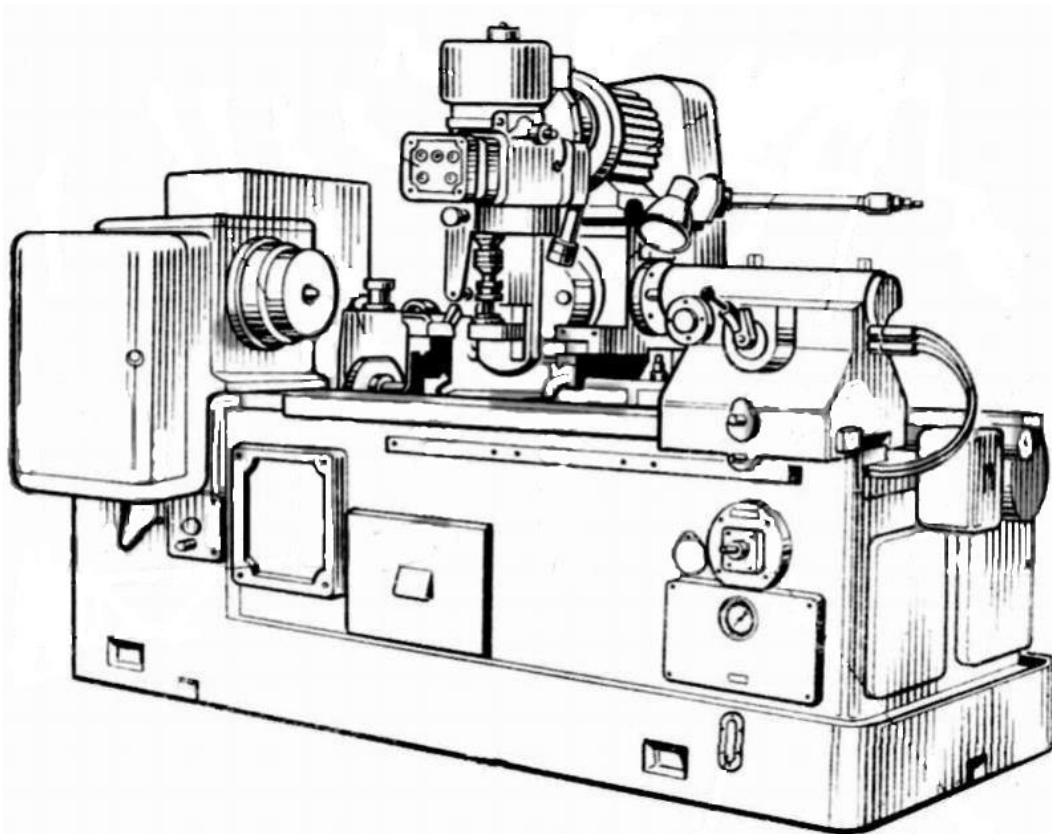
Загальний вид шліцефрезерного напівавтомату моделі 5350
